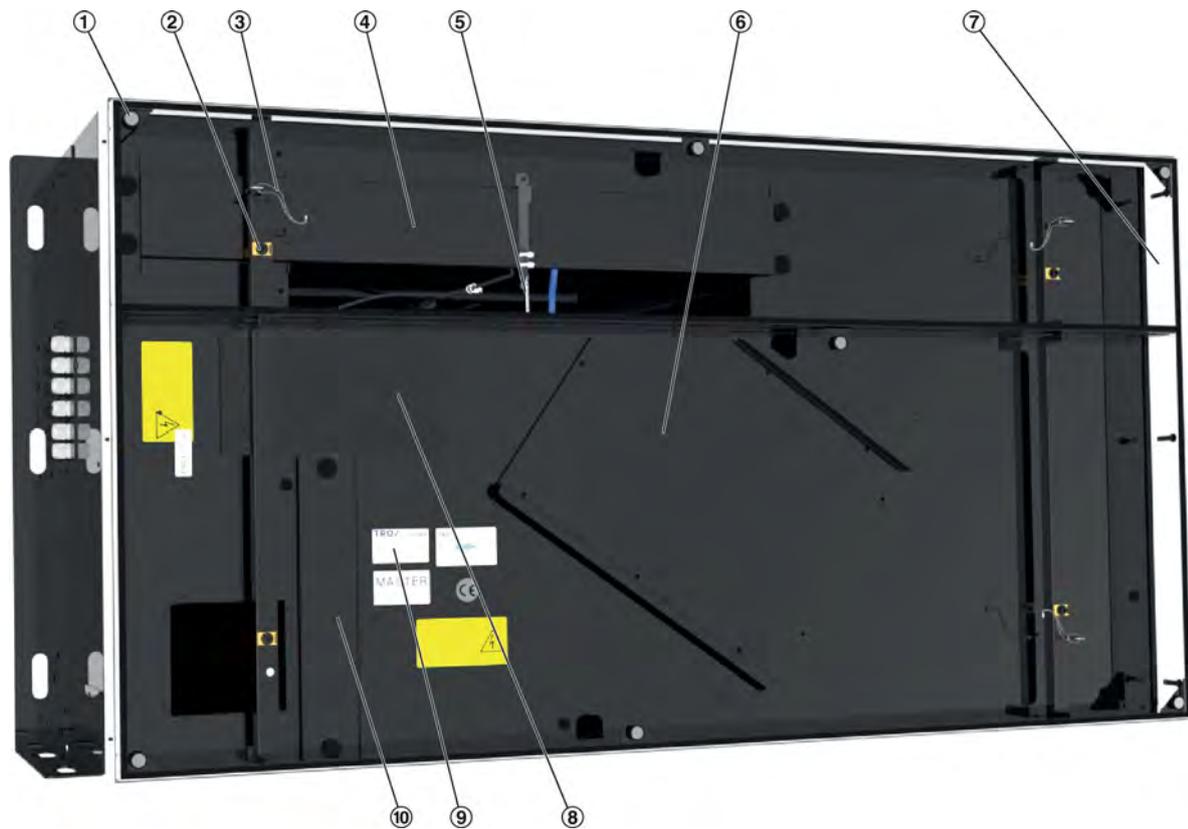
SCHOOLAIR-D (Deckenanschlussplatte demontiert)
